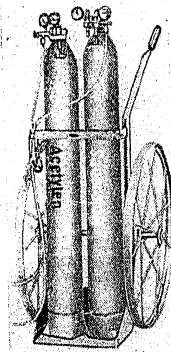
Fahrbare Azetylen-Sauerstoff-Schweißanlage
